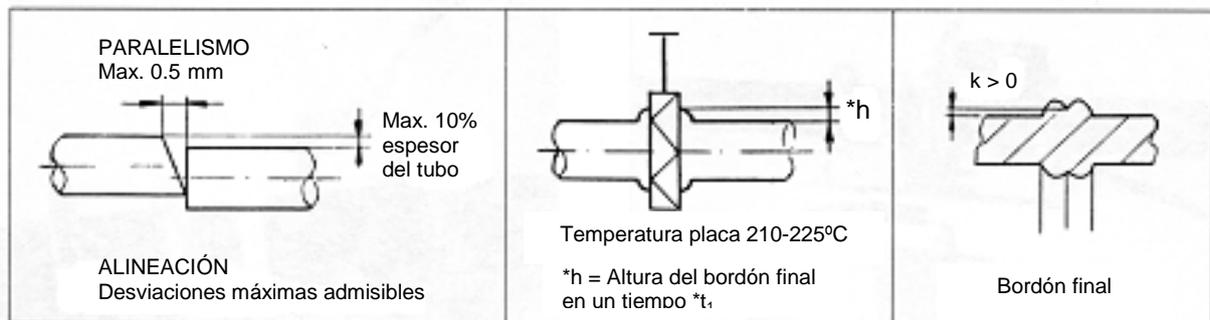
Parámetros de soldadura a tope según UNE 53394 (DVS 2207-1)
